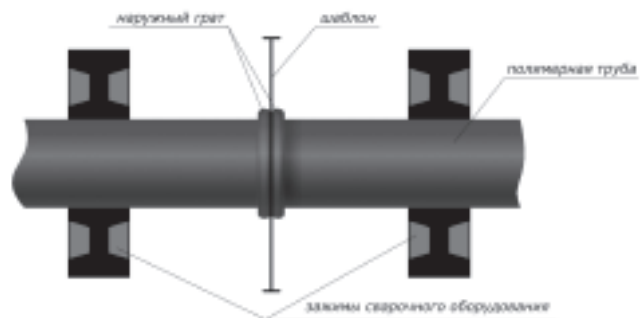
Схема охлаждения сварного соединения под давлением осадки
